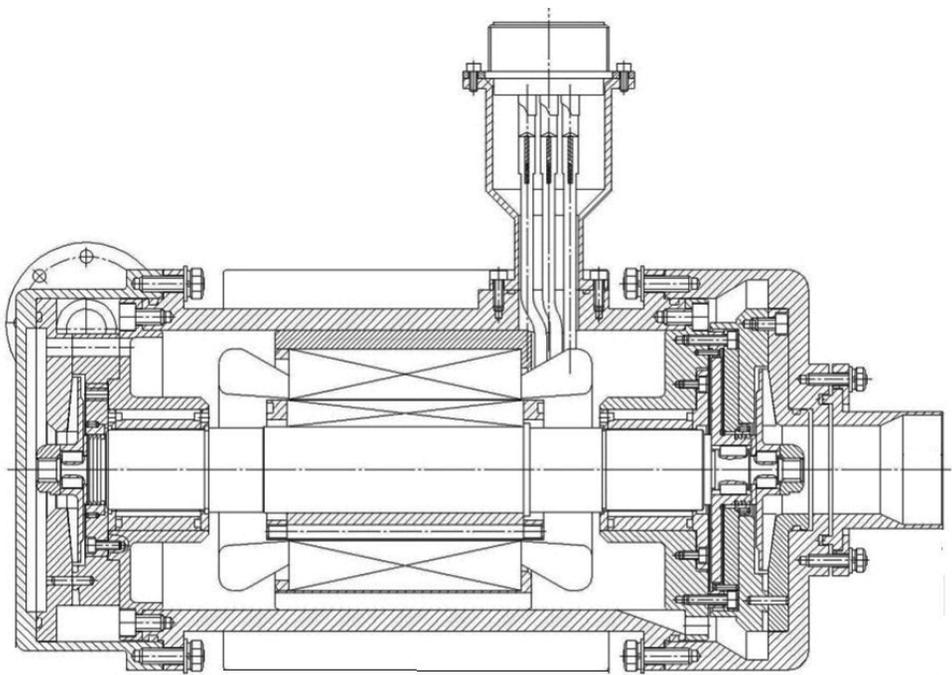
Малорасходный хладоновый двухступенчатый центробежный компрессор
